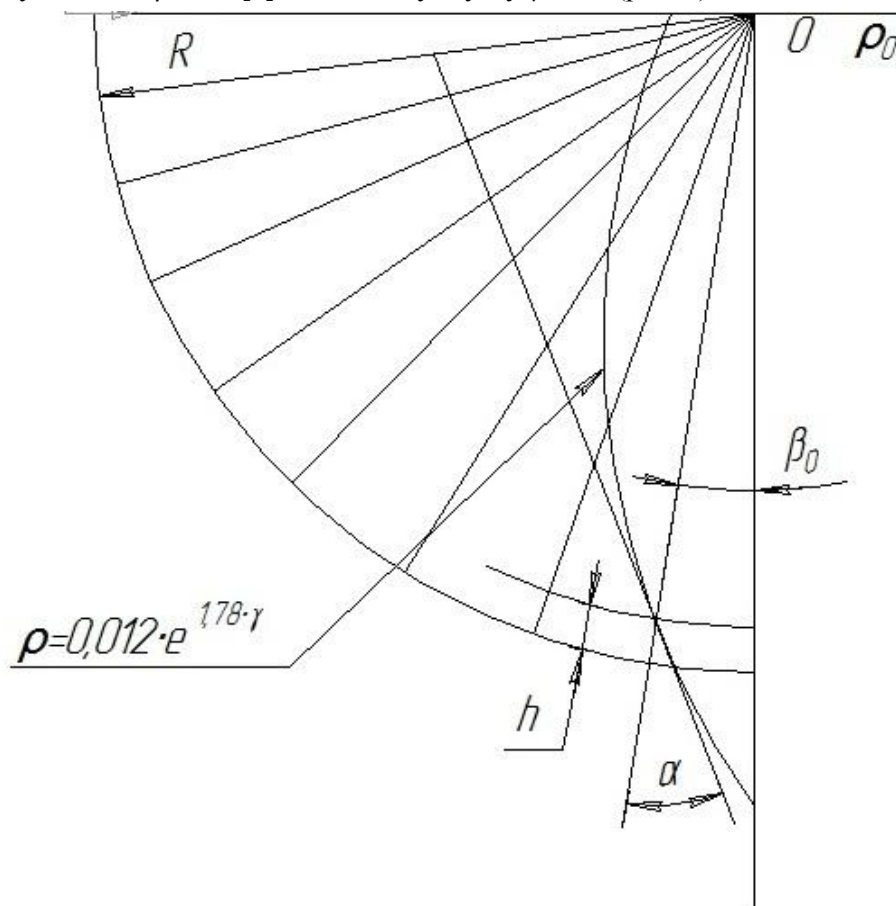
Построение профиля рабочей поверхности пластинчатого выталкивателя
